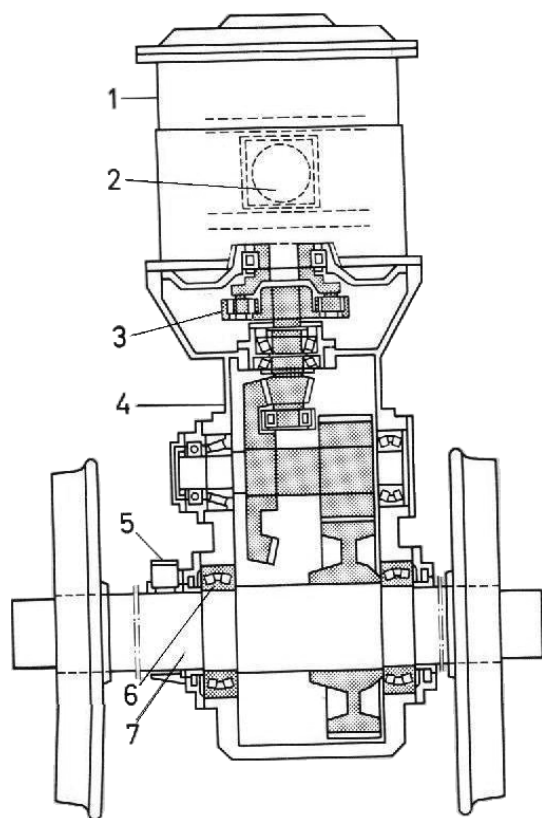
Конструкция подвески тягового электрического двигателя и трансмиссии шахтного электровоза фирмы ASEA (Швеция): 1 – двигатель; 2 – резиновая опора; 3 – эластичная муфта; 4 – редуктор; 5 – скользящий контакт; 6 – роликовый подшипник; 7 – ось колёсной пары
